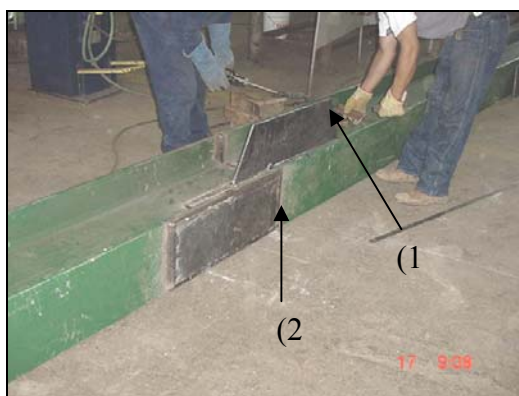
Soldado de plancha para juntas tubulares (1) y plancha de refuerzo en unión de viga H (2)... [1].
